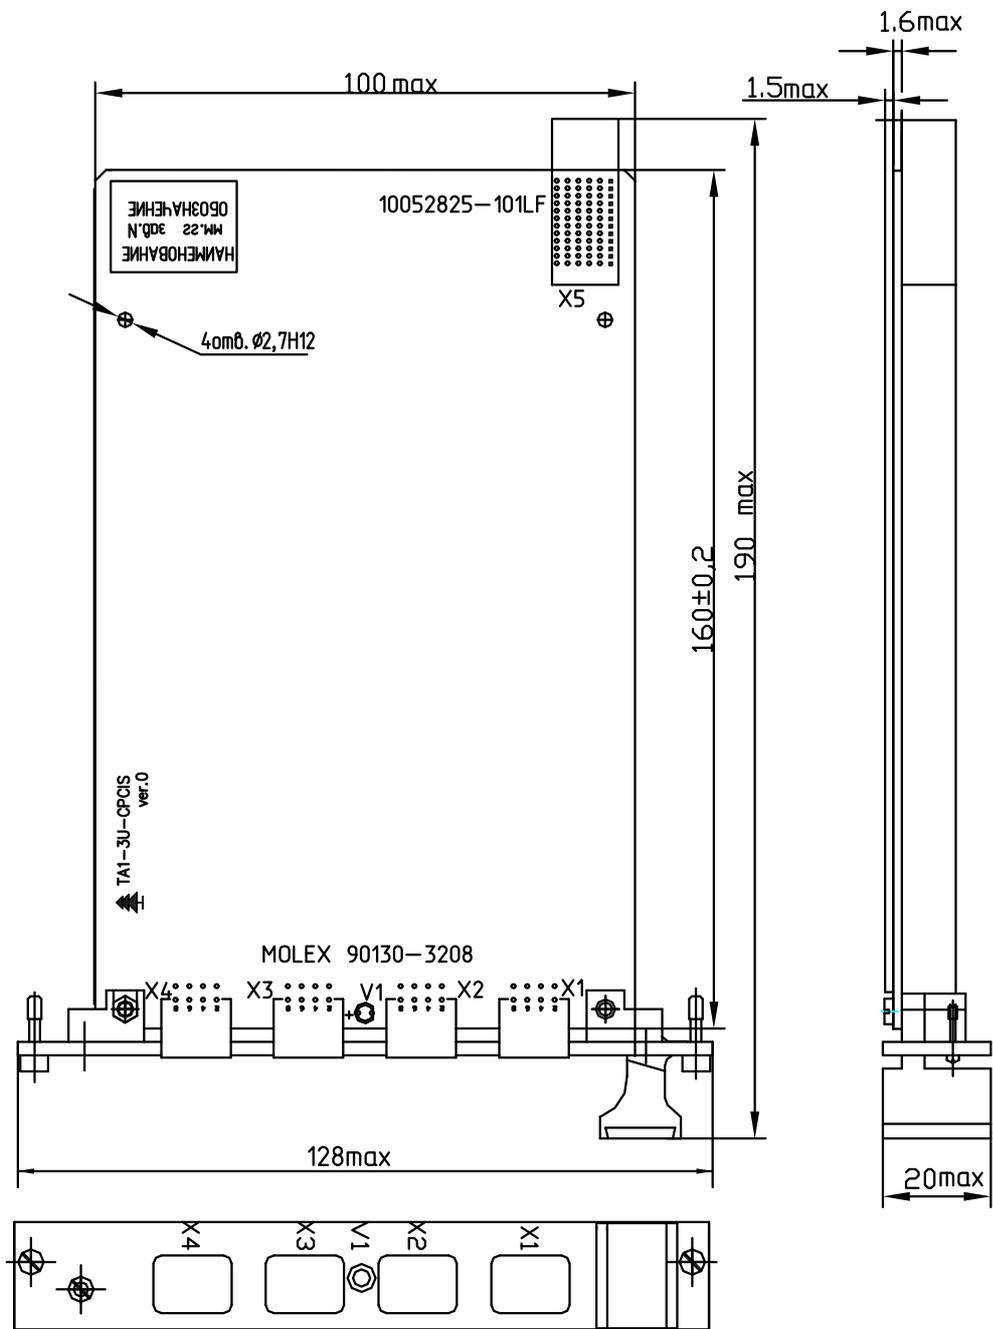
Габаритный чертеж изделия ТА1-3U-CPCIS ГФКП.468351.057(-01, -02)
